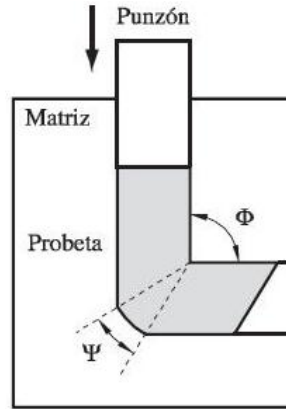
1 Proceso de extrusión de canal angular constante [28].
